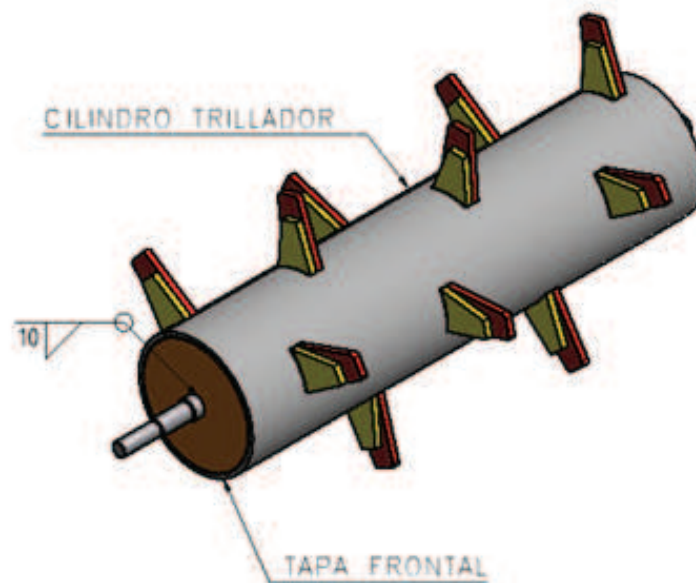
Detalle de la soldadura en la tapa
